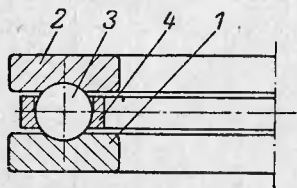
Шариковый упорный однорядный подшипник, тип 8000.
